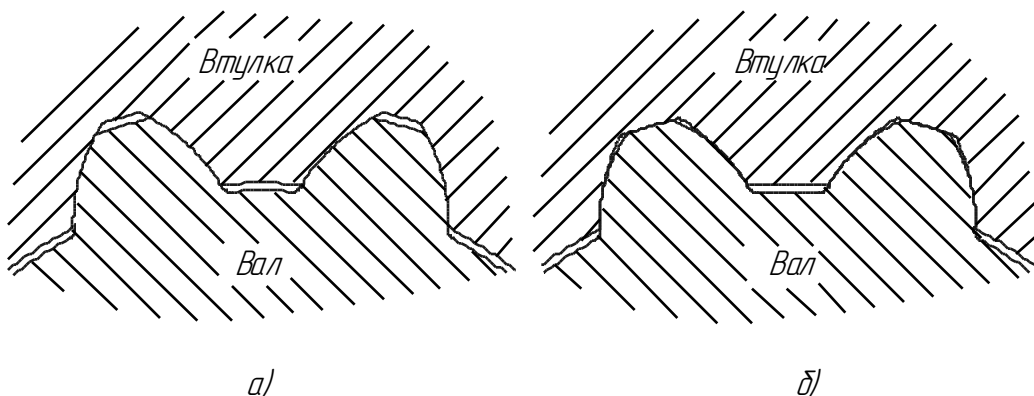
Способы центрирования прямобочных шлицевых соединений
